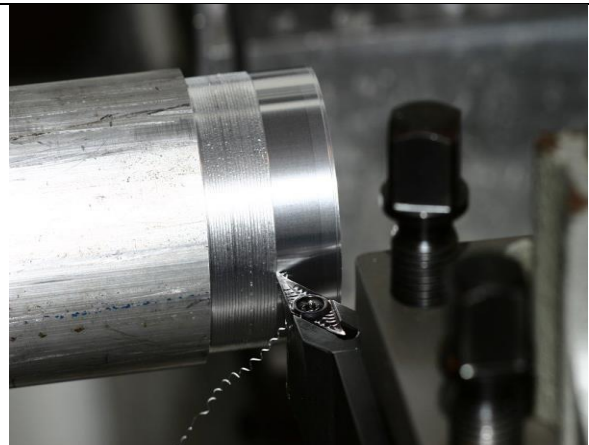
Токарна обробка зовнішньої циліндричної поверхні
